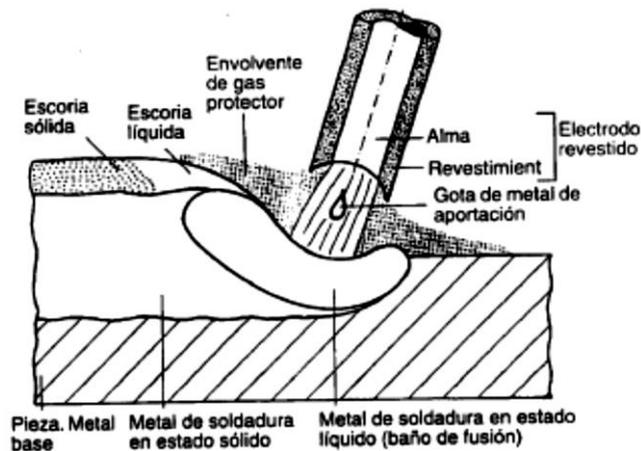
Variables que intervienen en el proceso de soldadura SMAW
